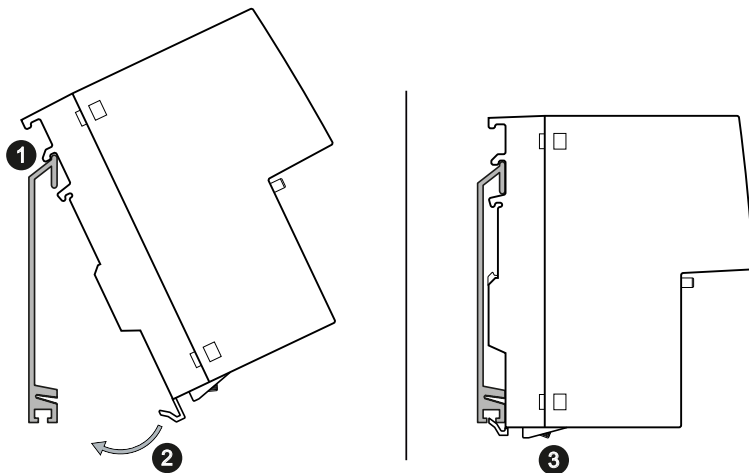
S7-300 Profilschienenmontage mit dem Befestigungsriegel in der Wandmontageposition
